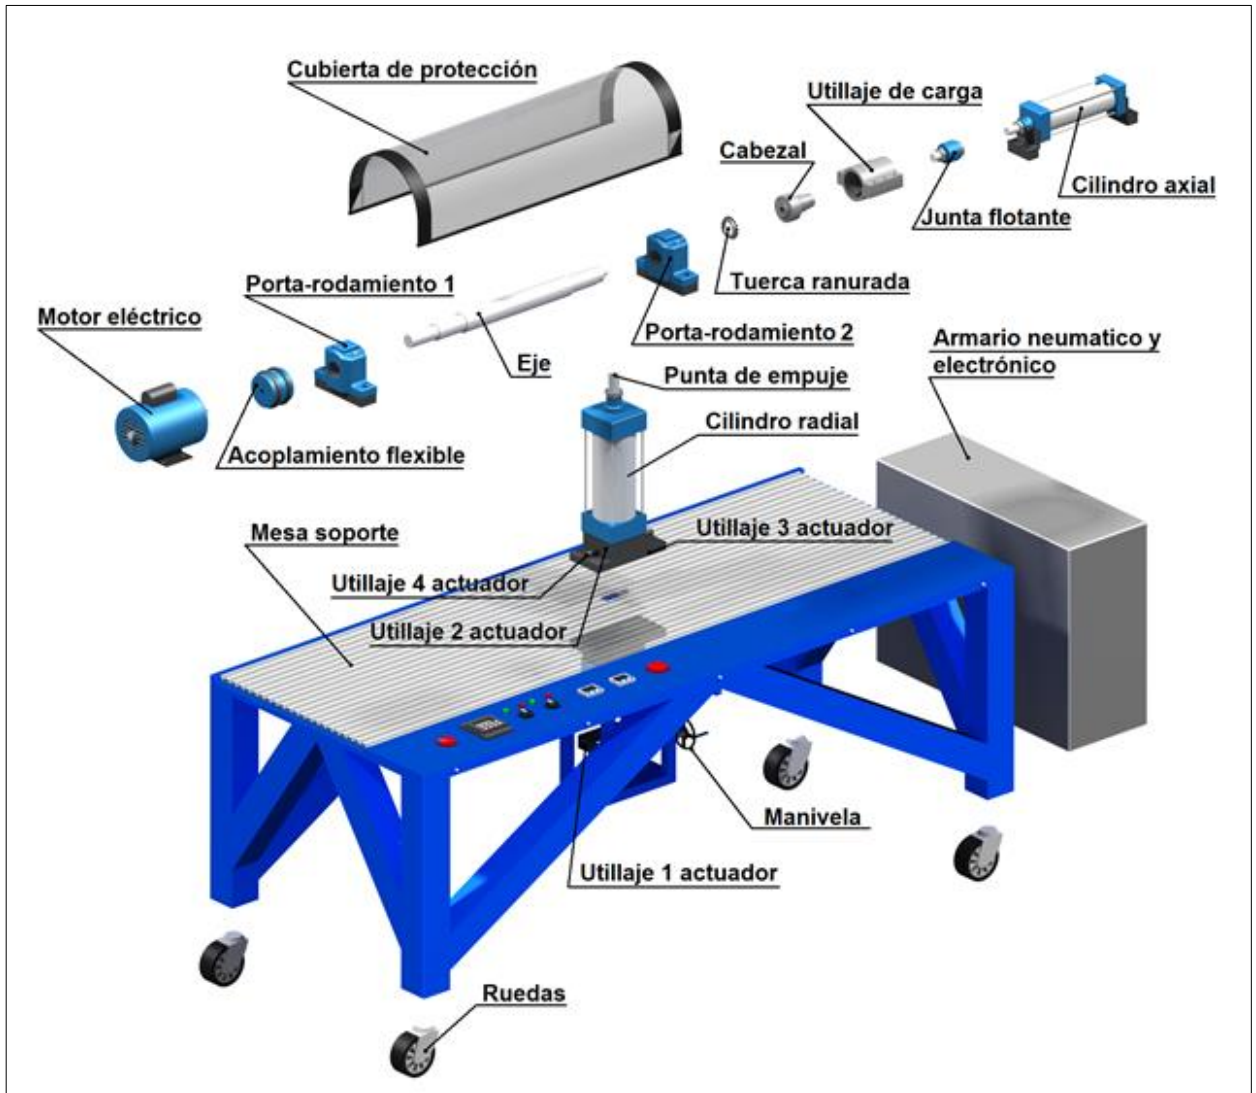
Explosionado del banco de ensayo de rodamientos
